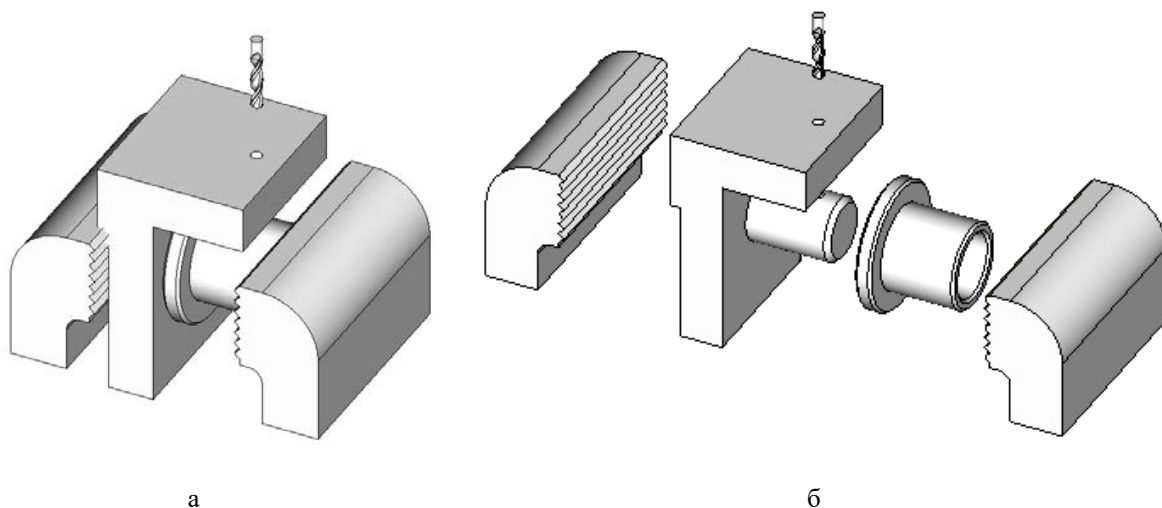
а, б. Вариант конструкции приспособления для сверления в тисках:
